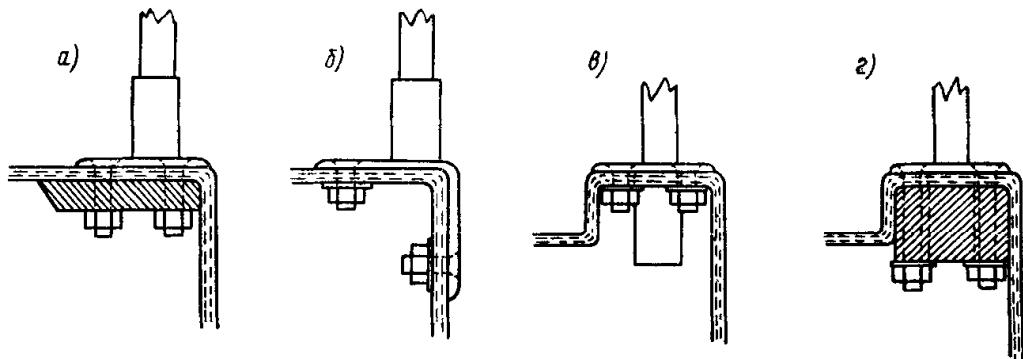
Крепление стоек леерного ограждения к палубе болтами: *а* — с установкой снизу подкладной планки; *б* — усиленное соединение с креплением отогнутой части основания к борту; *в* — крепление осиования проходящего сквозь палубу гнезда к отформованному предохранительному буртику; *г* — усиленное крепление пропущенного сквозь палубу гнезда с использованием подкладки из дерева, шпаклевки, синтактного пеопласта или в виде сплошной формованной детали.
